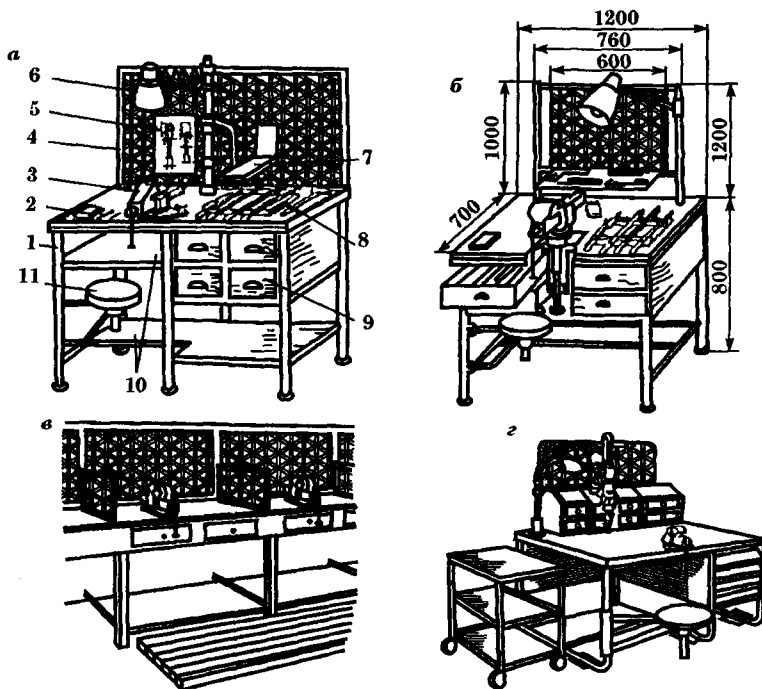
Верстаки: *а* — одностенный с нерегулируемыми по высоте тисками; 1 — каркас; 2 — столешница; 3 — тиски; 4 — защитный экран; 5 — планшет для чертежей; 6 — светильник; 7 — полочка для инструментов; 8 — планшет для рабочего инструмента; 9 — ящики; 10 — полки; 11 — сиденье; *б* — одностенный с регулируемыми по высоте тисками; *в* — многостенный; *г* — одностенный с передвижным сборочным столиком и приспособлением для подвески механизированного инструмента
